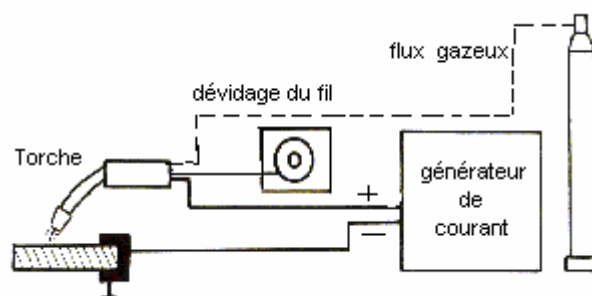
Schéma d'installation du dispositif de soudage
